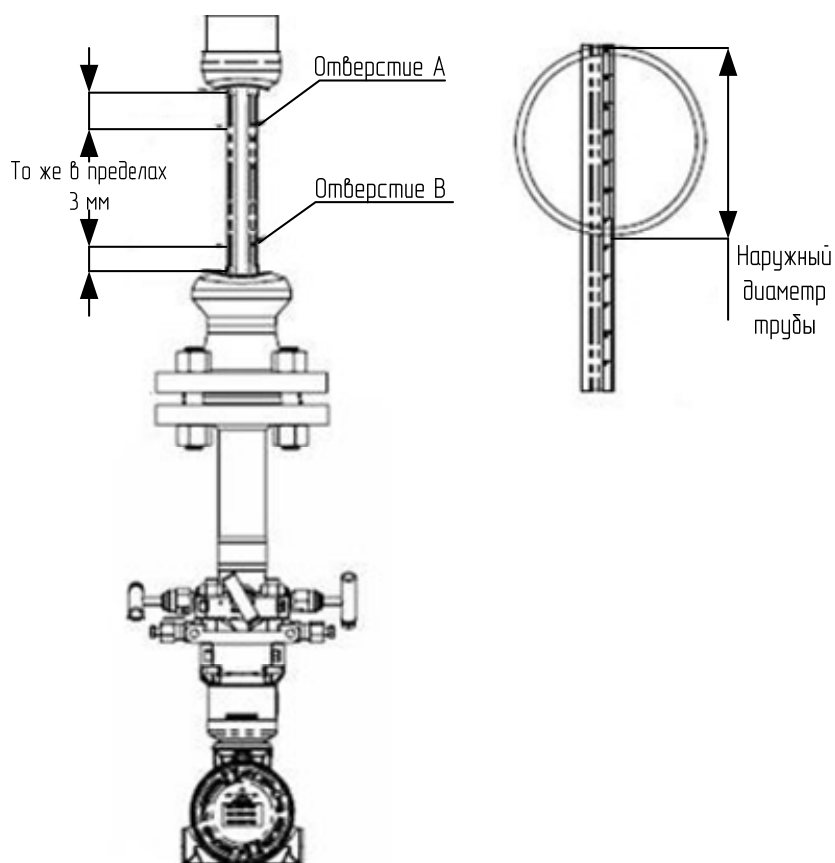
Проверка сборки ОНТ, монтажного фланца и опоры с противоположной стороны
